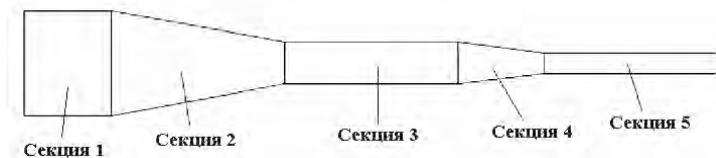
Комбинированный многоступенчатый ультразвуковой концентратор-инструмент
